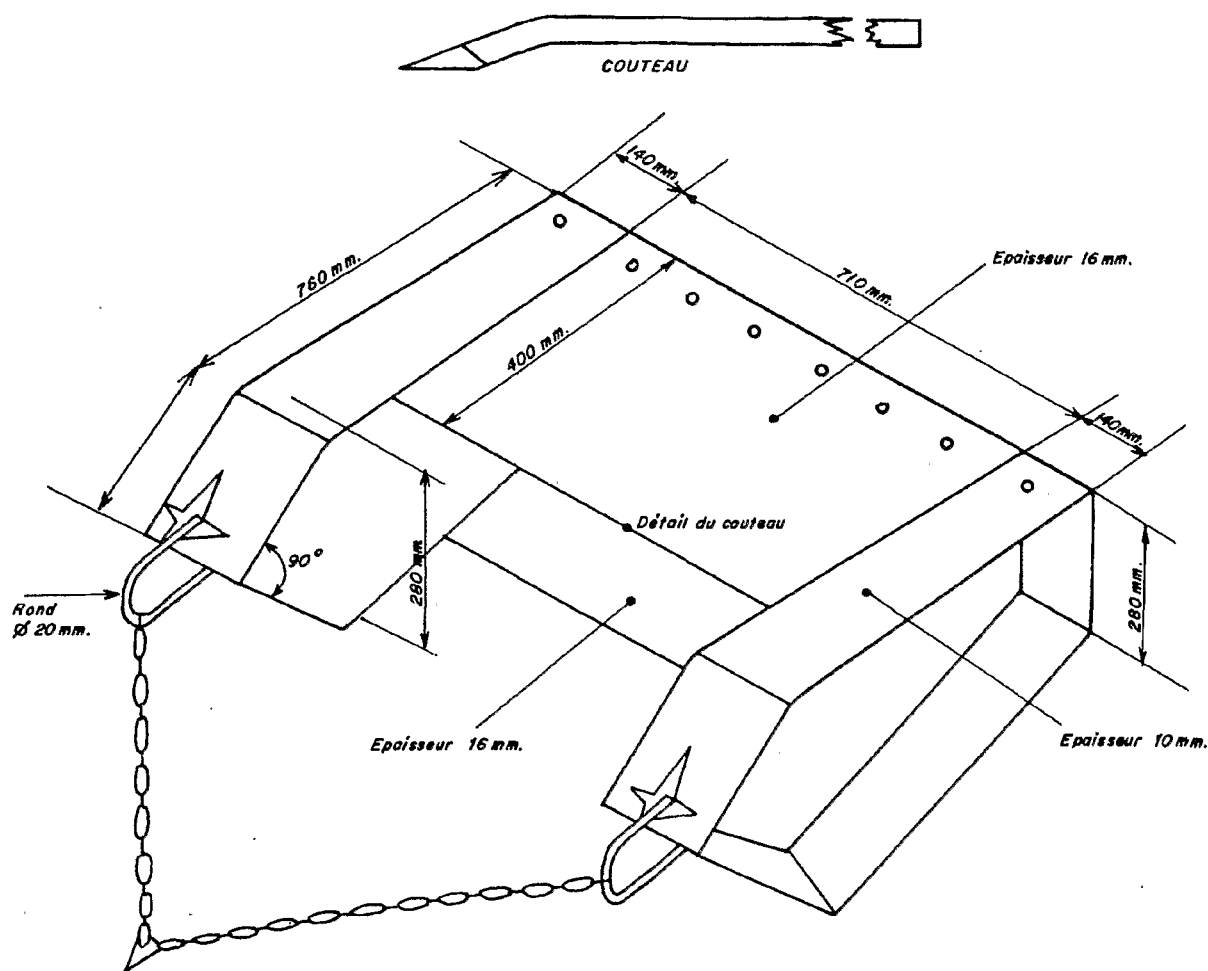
Plan du cadre métallique d'une drague WAREN.
